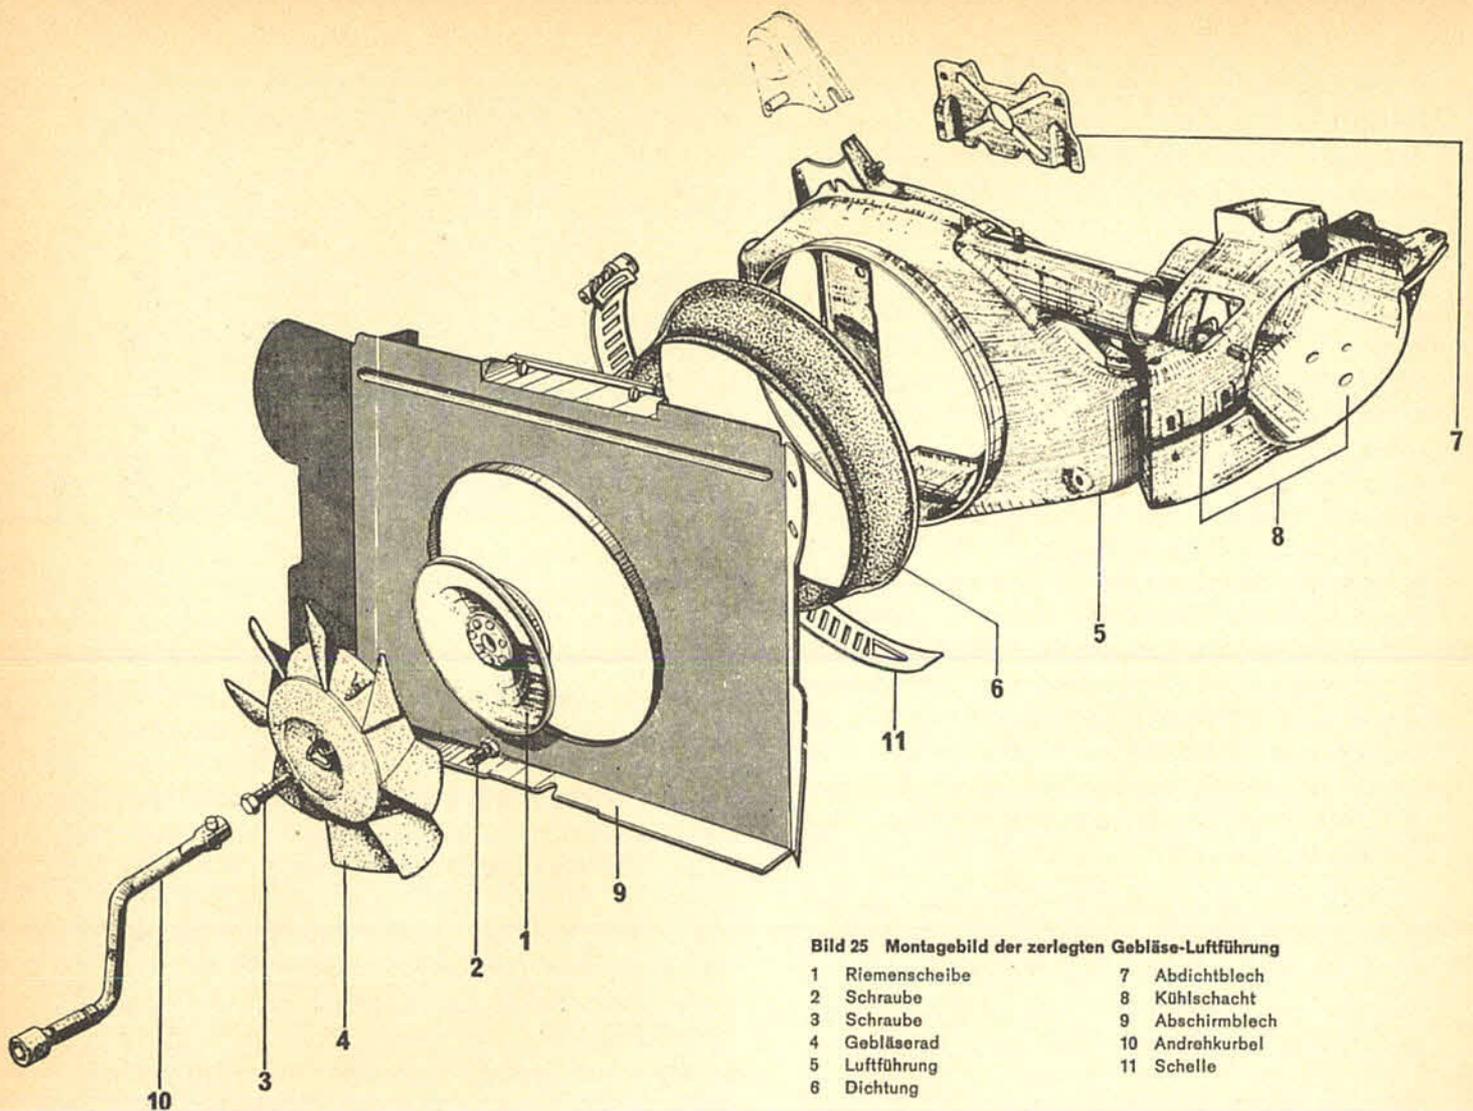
Montagebild der zerlegten Gebläse-Luftführung
